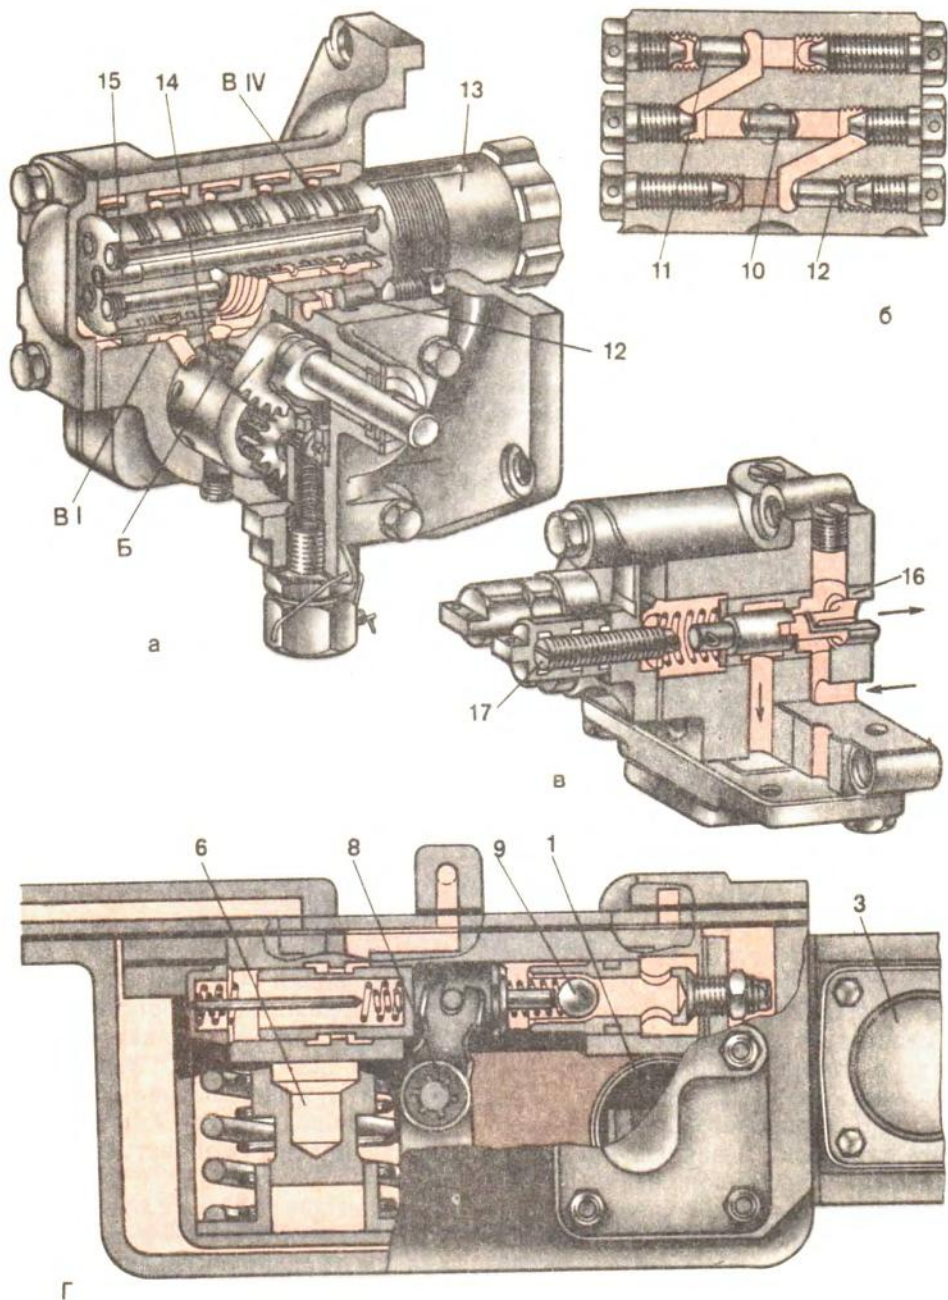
Гидроагрегаты коробки передач трактора Т-150:
